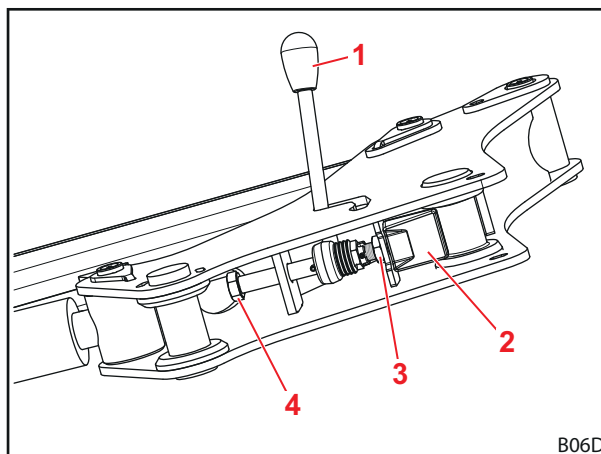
Vederea de jos a dispozitivului de blocare încărcător frontal
